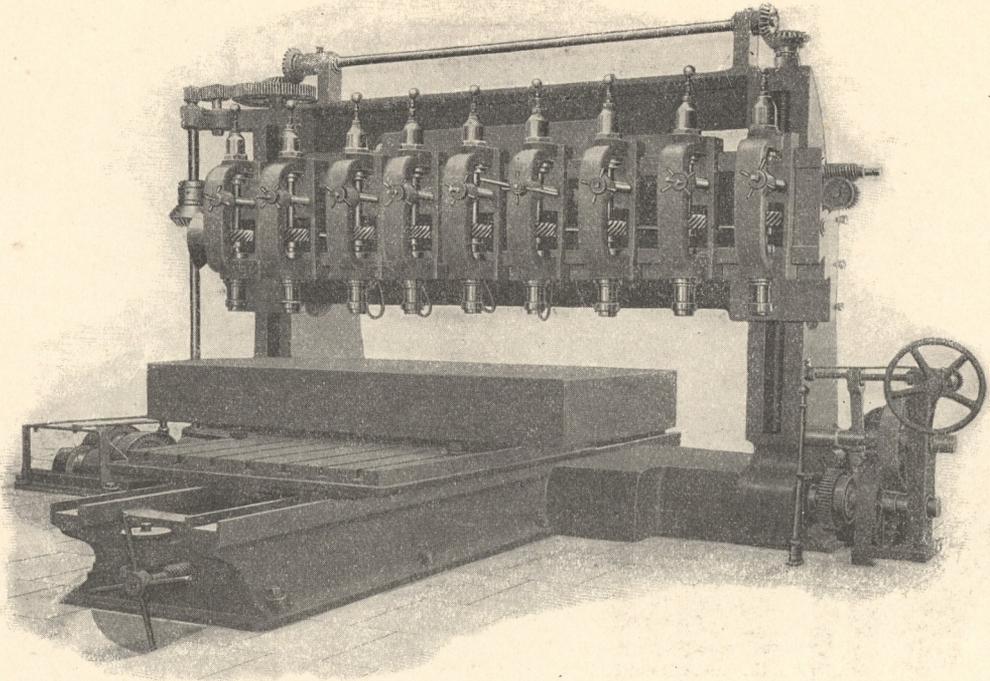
Neunspindlige Bohrmaschine zum Bohren von Wasserkammern.
